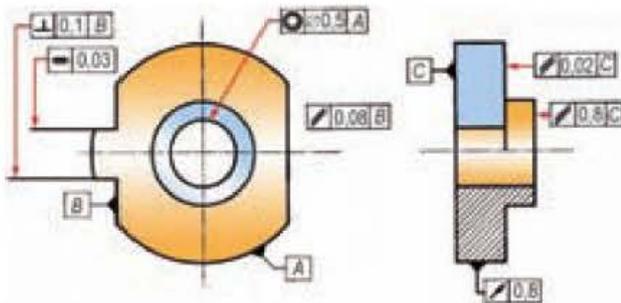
Ejemplo de especificación de tolerancias geométricas.
